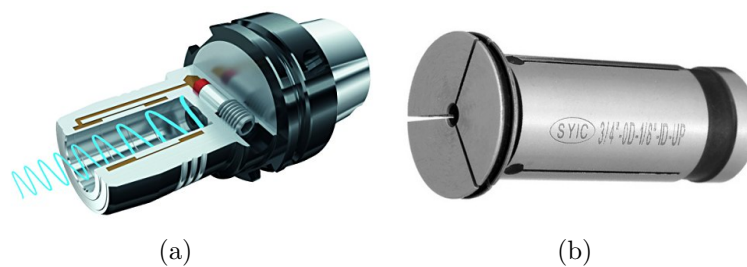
a) Corte porta herramienta ; b) Boquilla reductora
